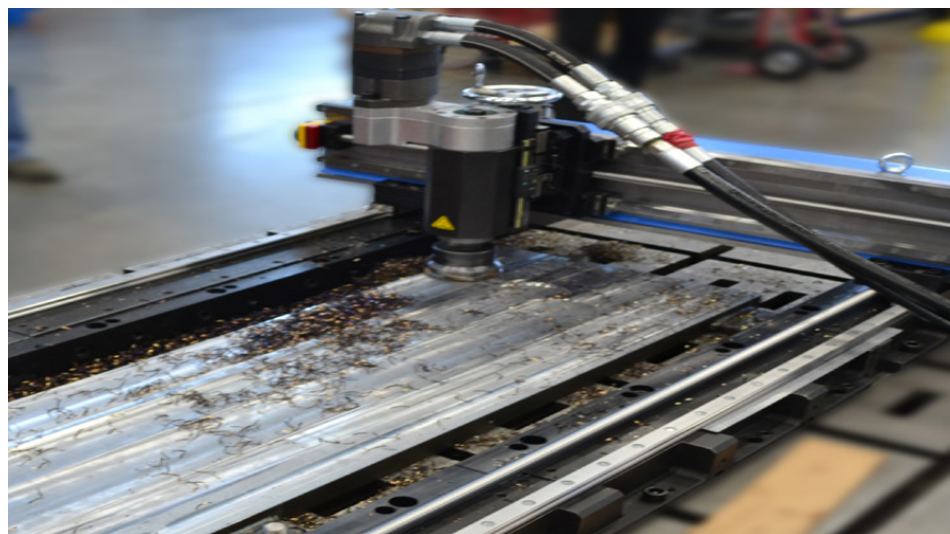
Мобільний фрезерний верстат LM5200
